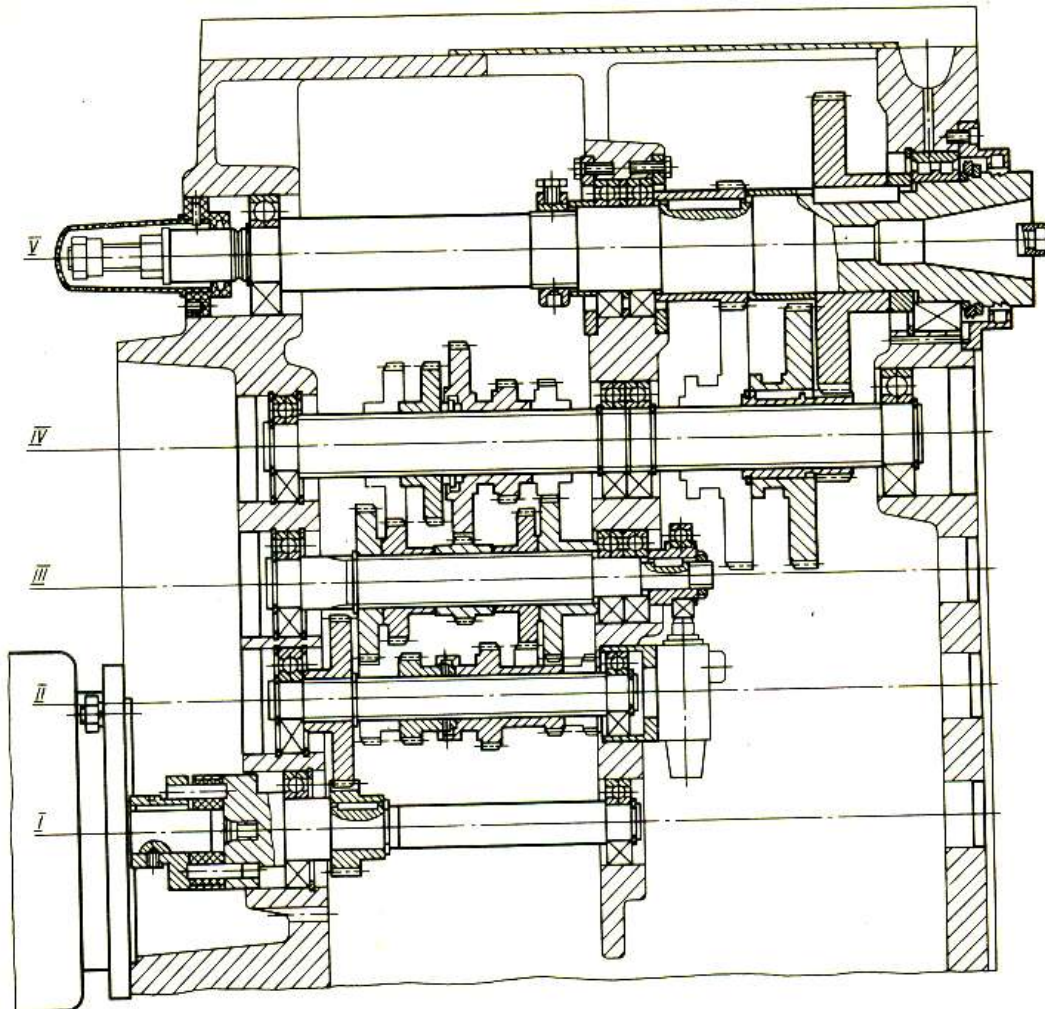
Коробка швидкостей широкоуніверсального фрезерного верстата
